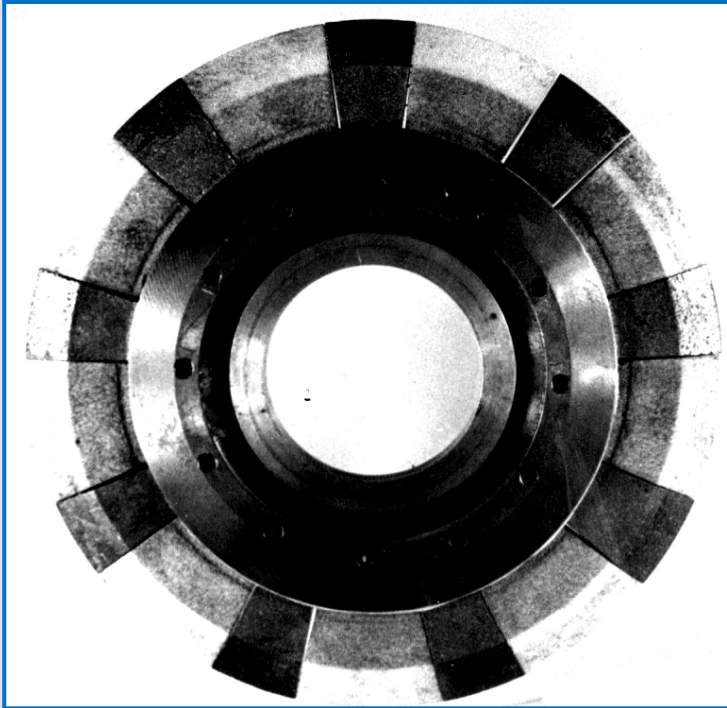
Сборный композиционный круг для профильного зубошлифования
